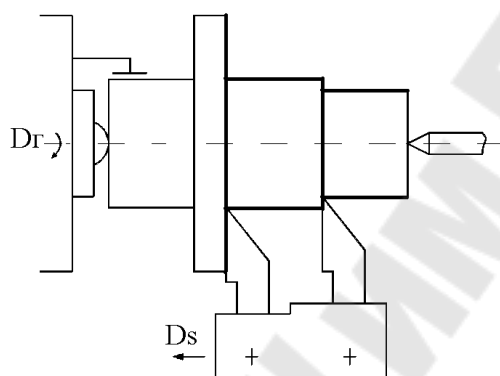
Схема обработки цилиндрических поверхностей вала за один переход
